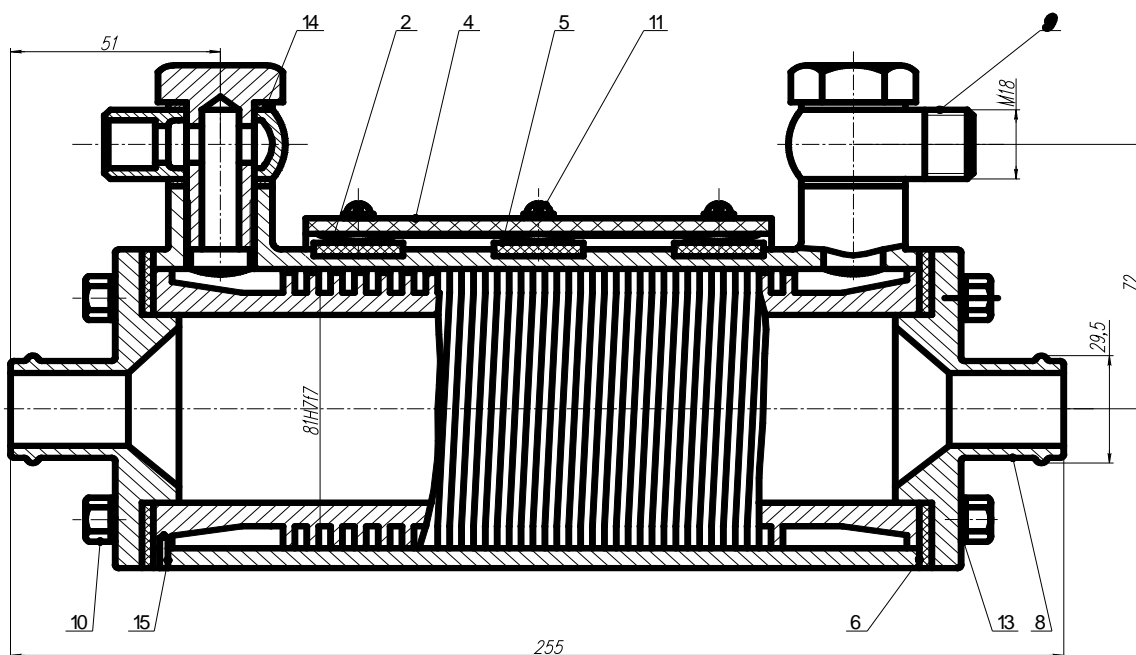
Нагрівач біопалива: 1- корпус; 2,3 - патрубки для підведення і відведення палива відповідно; 4 - теплопередаючий елемент; 5,6 - фланці для циркуляції вихлопних газів; 7 - штифт; 8 - гвинтові ребра; 9 - гвинтові канали; 10 - позистори; 11- контактні пластини; 12 - кришка; 13 - гвинти; 14 -вершини ребер; 15-подовжні канали (зазор).
